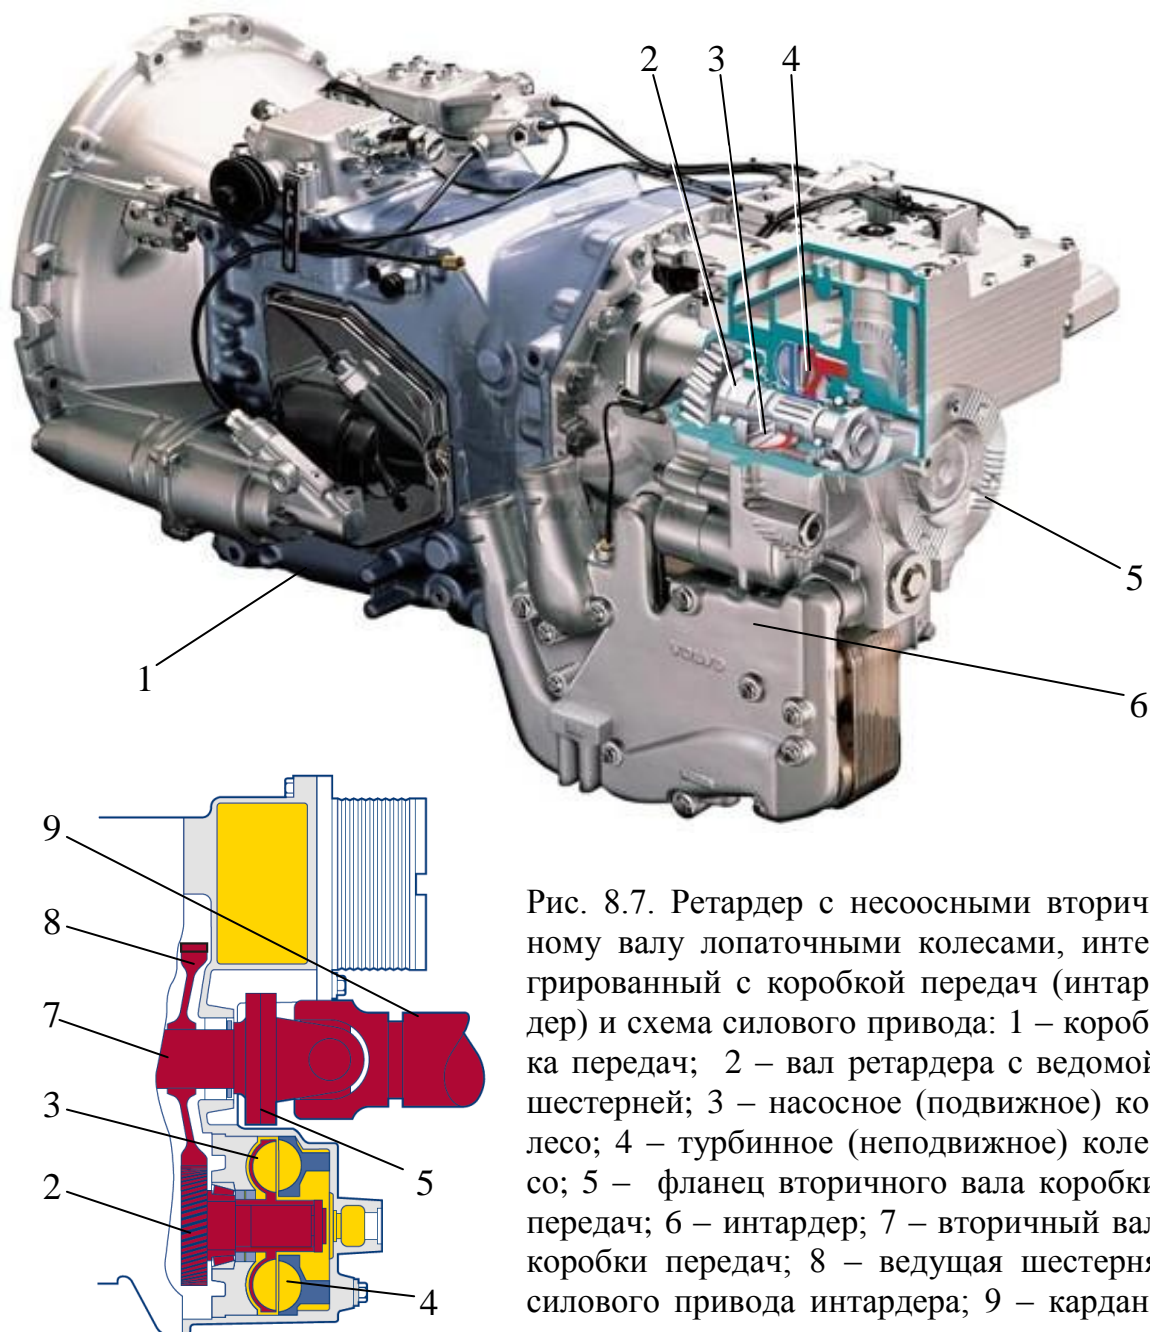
Ретардер с несоосными вторичному валу лопаточными колесами, интегрированный с коробкой передач (интардер) и схема силового привода: 1 – коробка передач; 2 – вал ретардера с ведомой шестерней; 3 – насосное (подвижное) колесо; 4 – турбинное (неподвижное) колесо; 5 – фланец вторичного вала коробки передач; 6 – интардер; 7 – вторичный вал коробки передач; 8 – ведущая шестерня силового привода интардера; 9 – карданная передача
